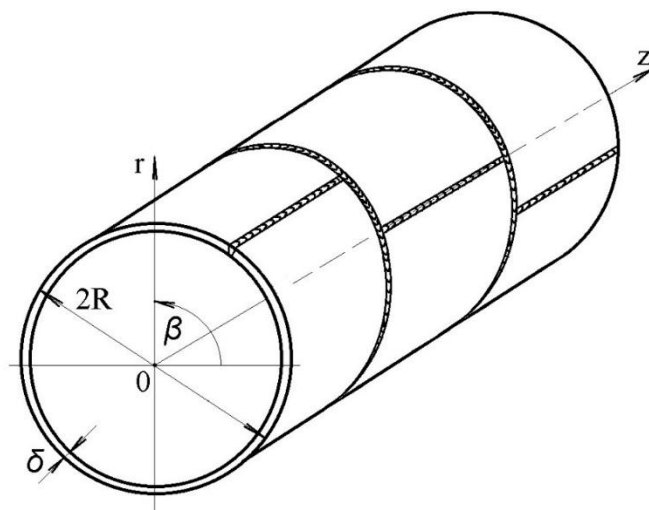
Схема зварної циліндричної оболонки в циліндричній системі координат  $(r, \beta, z)$
